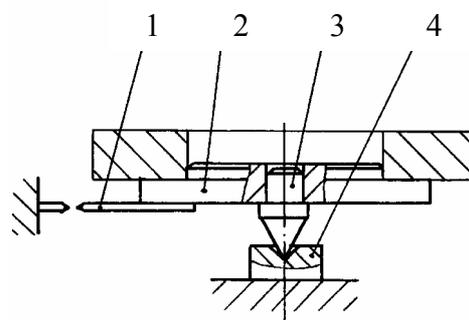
Схема устройства для статической балансировки деталей на качающемся диске:
